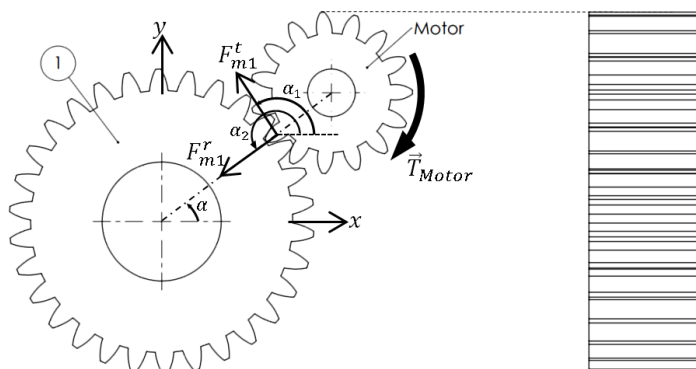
Interação de força entre as engrenagens do motor e a engrenagem (1)
